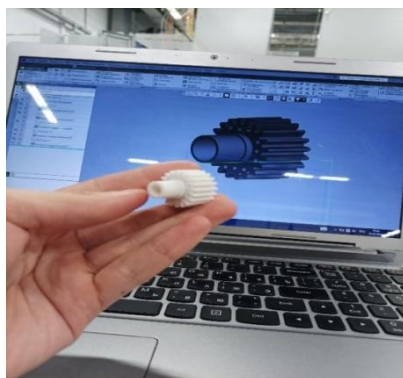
Распечатанная модель шестерни на 3D-принтере.
